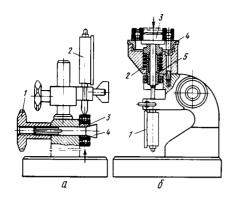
Приспособления для измерения зазоров в подшипниках качения:
